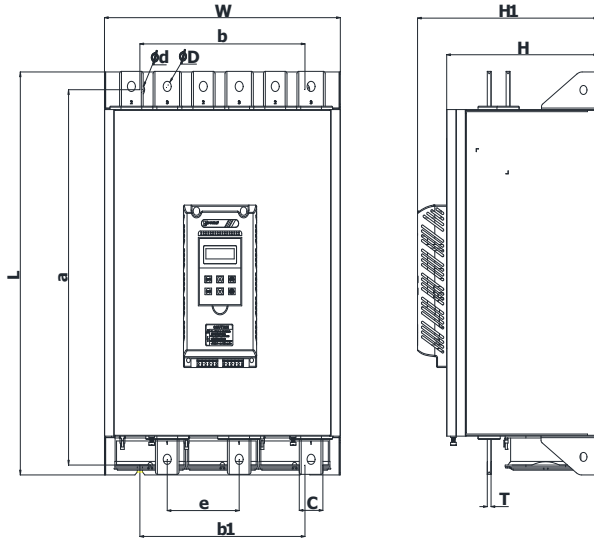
PR5300G3 500kW 外形尺寸 (机座号: F05)
